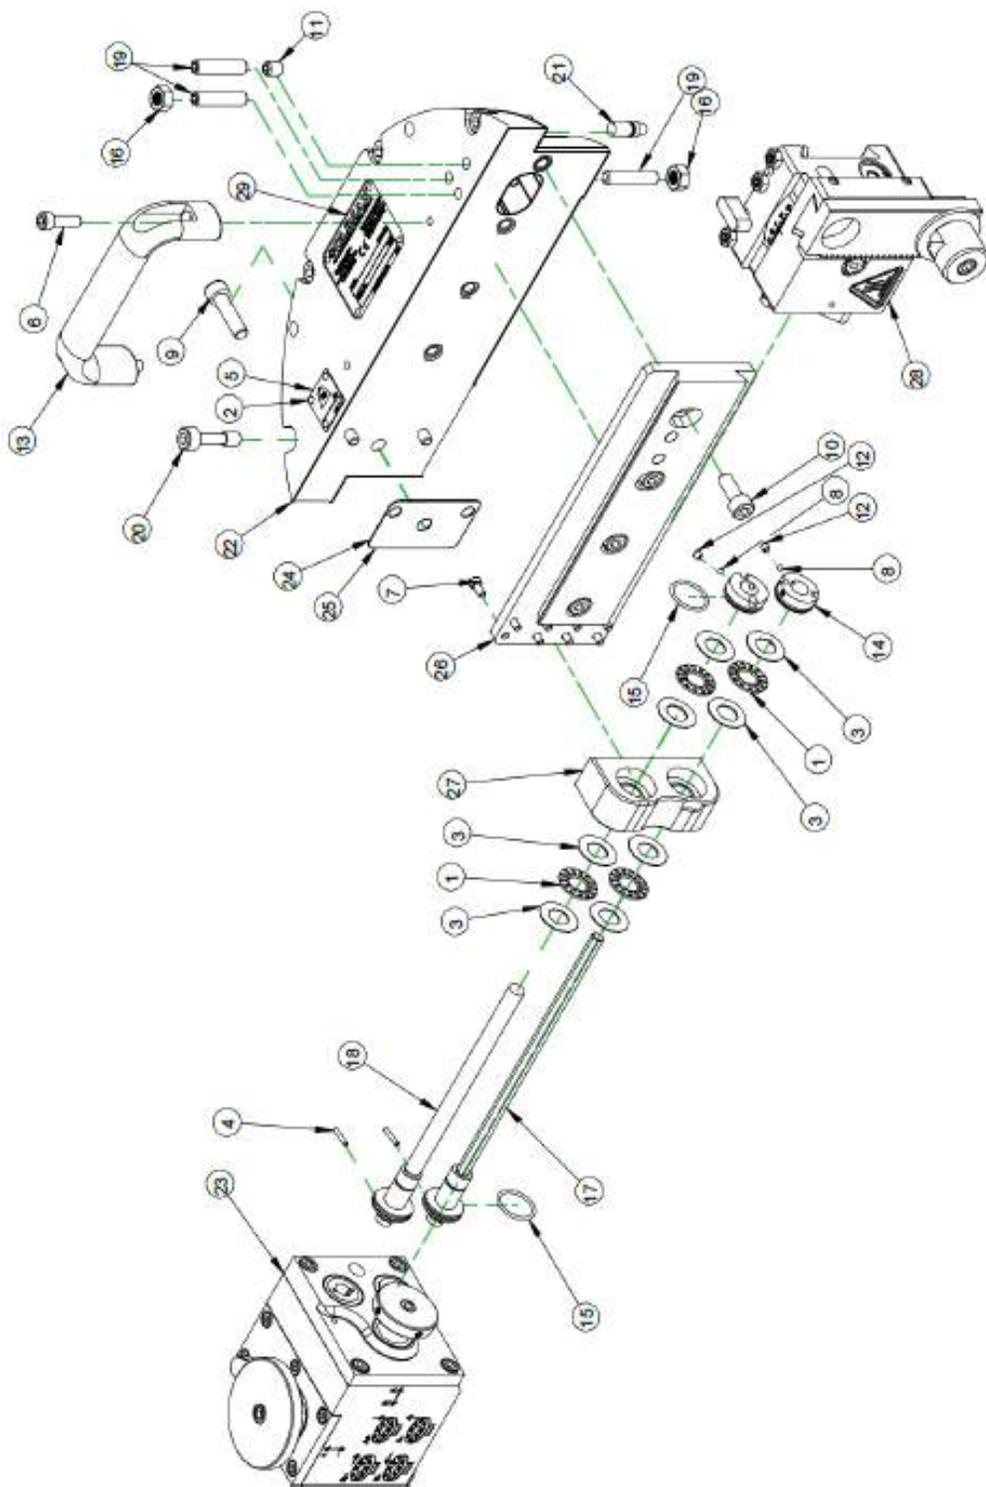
ENSEMBLE DE GLISSIÈRE RADIALE ET AXIALE FF1200 (RÉF. 79192)
